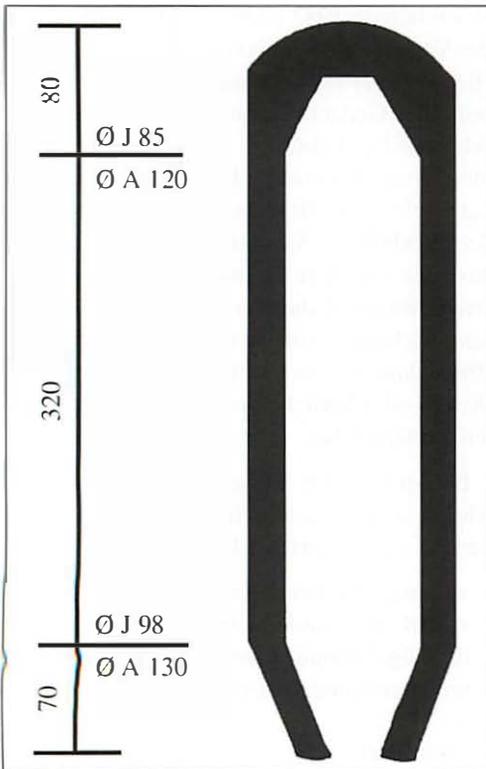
Schnitt durch den Holzbeton-Röhrenkasten (HI/Typen Fa-c) mit Abmessungen
